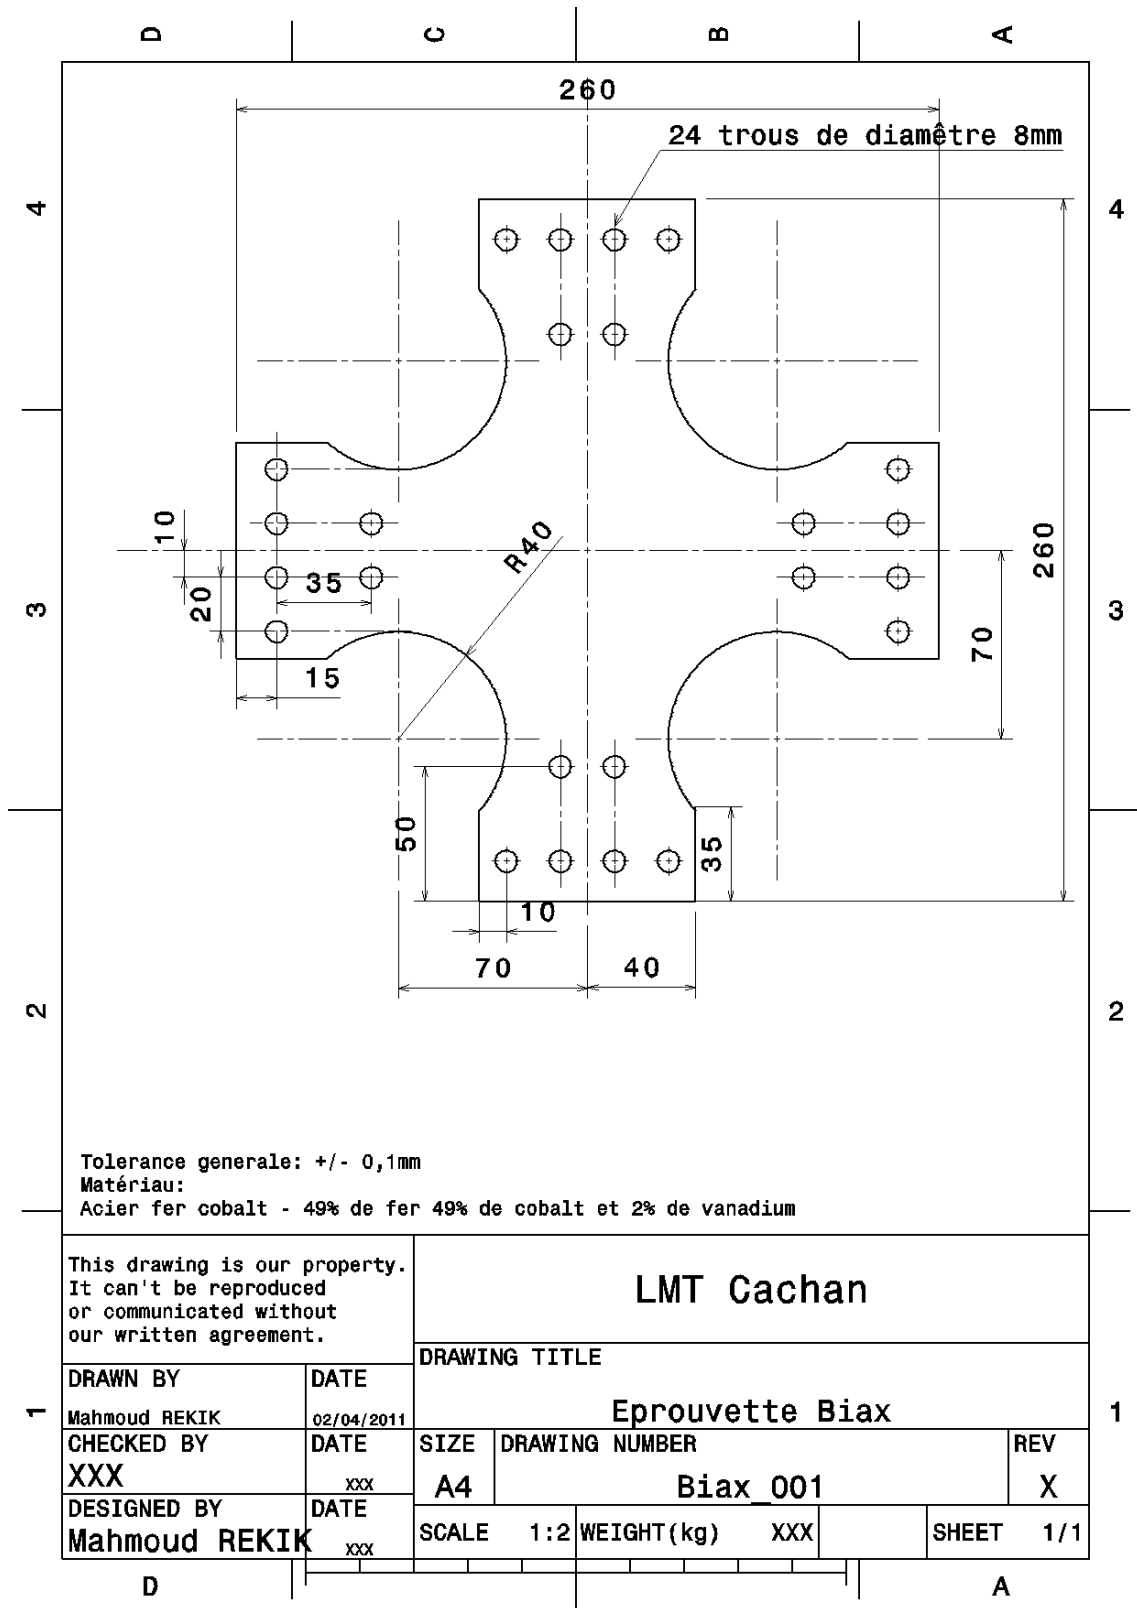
Dessin d'ensemble de l'éprouvette biaxiale.
